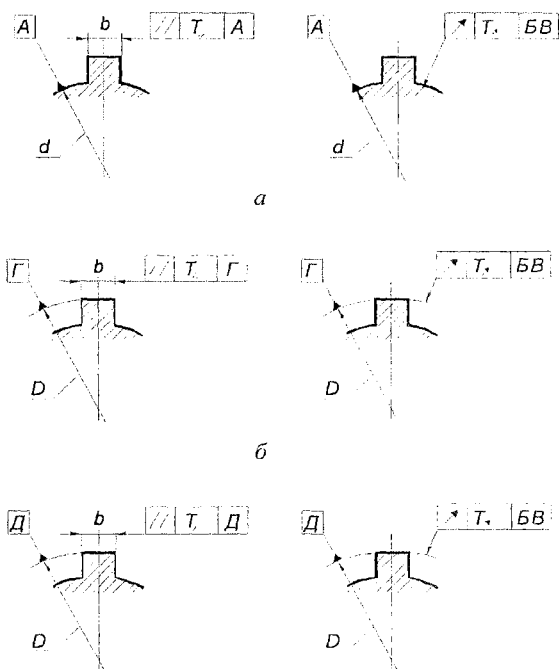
Обозначения допусков параллельности и радиального биения элементов наружной шлицевой поверхности:
